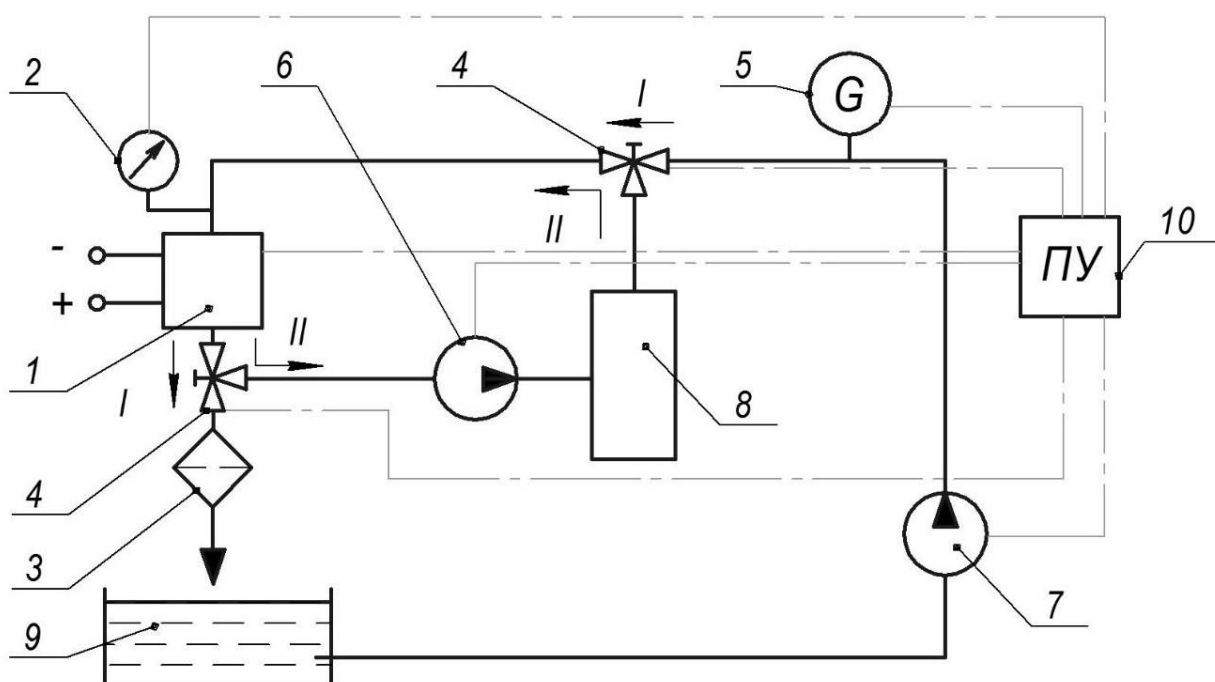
Робоча схема установки для комбінованої електрохімічної доведення деталей з малорозмірних щілинними каналами:
